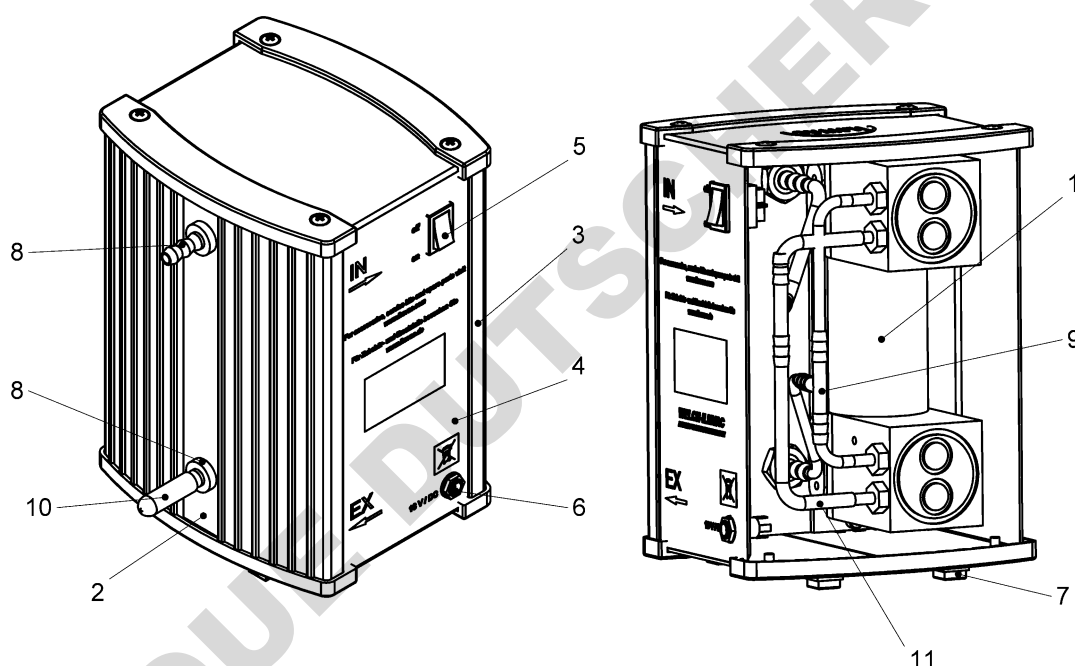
Pièces de rechange vue de devant et vue arrière (représenté sans paroi arrière)
